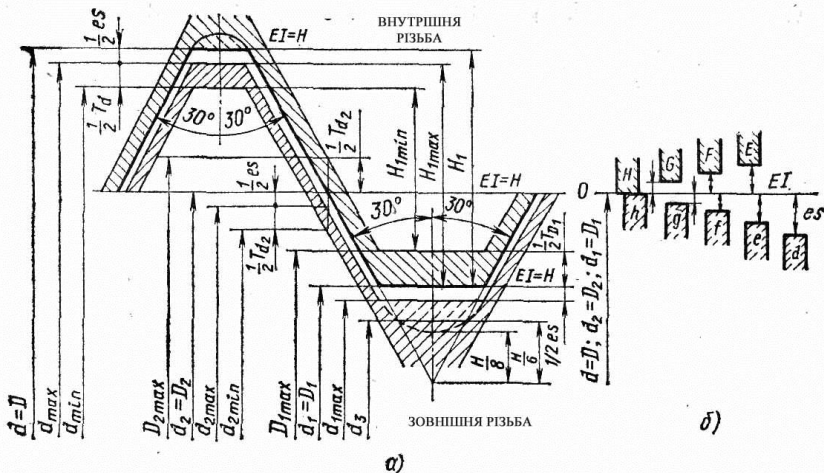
Метрична різьба із зазором: а) основні відхилення метричної різьби; б) розміщення полів допусків
